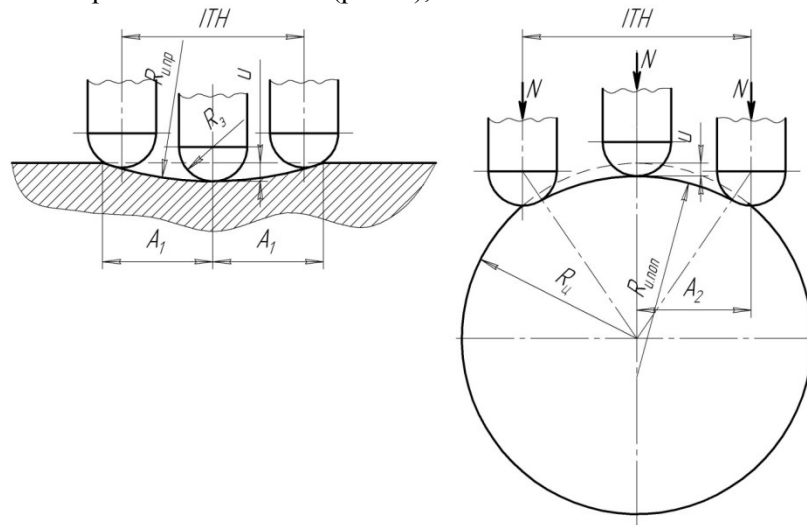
Контакт сферической заготовки с цилиндрической поверхностью установочной опоры
